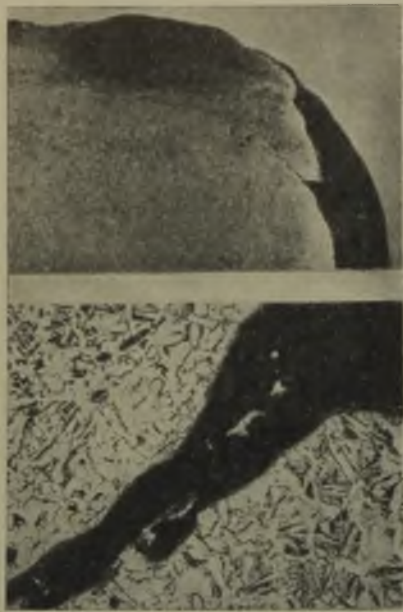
Kaltschweißstelle an der Fahrkante im Makro- und im Mikroschliff.
